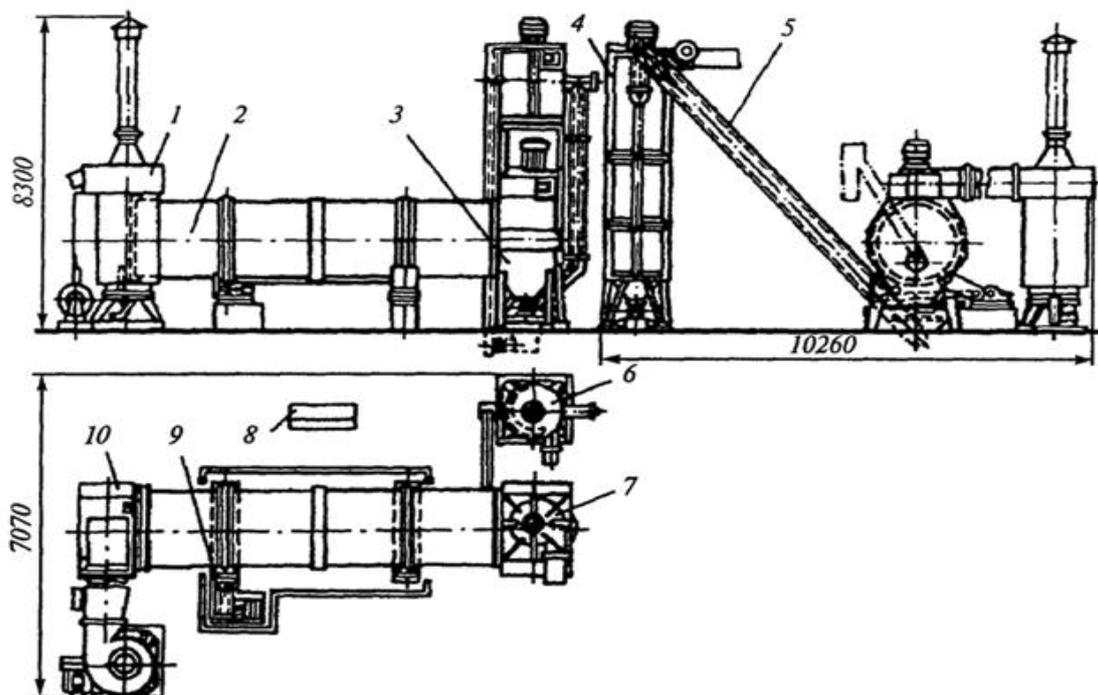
Зерносушилка ЗЗСБ-8
